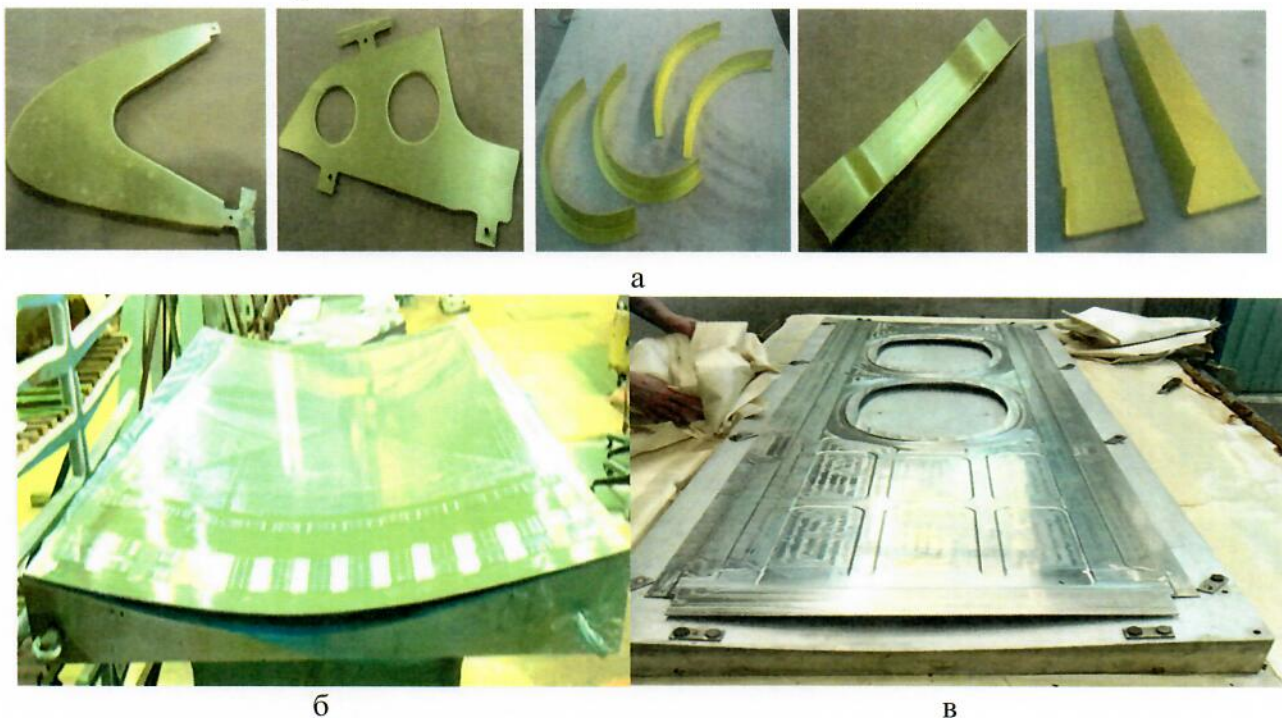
Детали из листов и профилей алюминий-литиевого сплава 1441 (а), фрагмент верхней обшивки крыла из алюминиевого сплава В950чТ2 (б), фрагмент нижней обшивки крыла из алюминий-литиевого сплава 1441Т1 (в)
